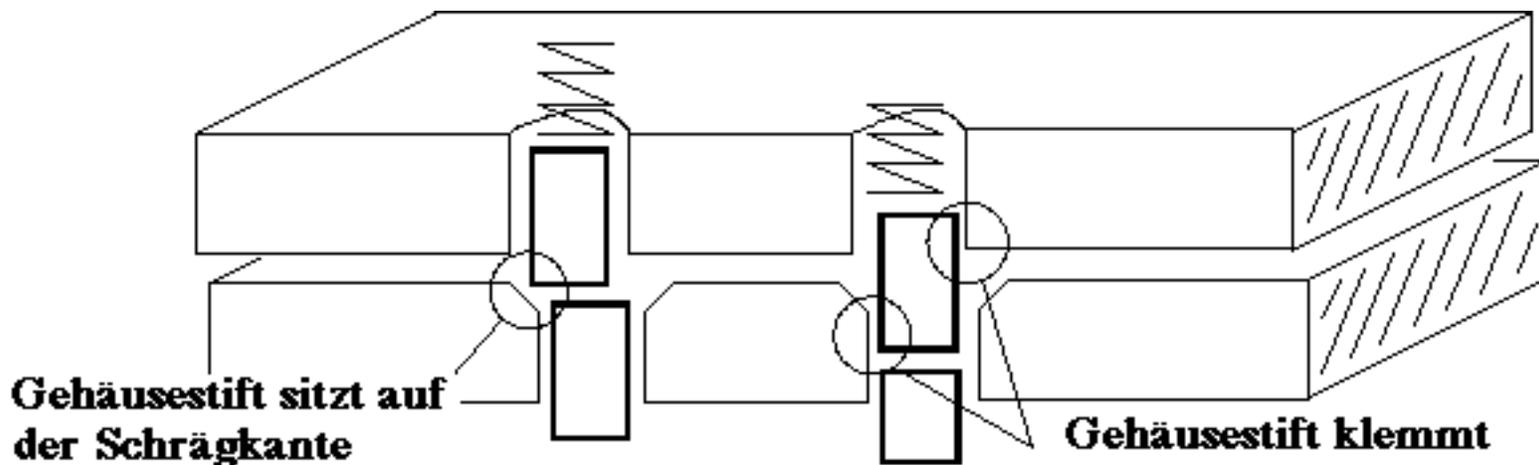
(a) Der Gehäusestift sitzt auf der Schrägfläche
